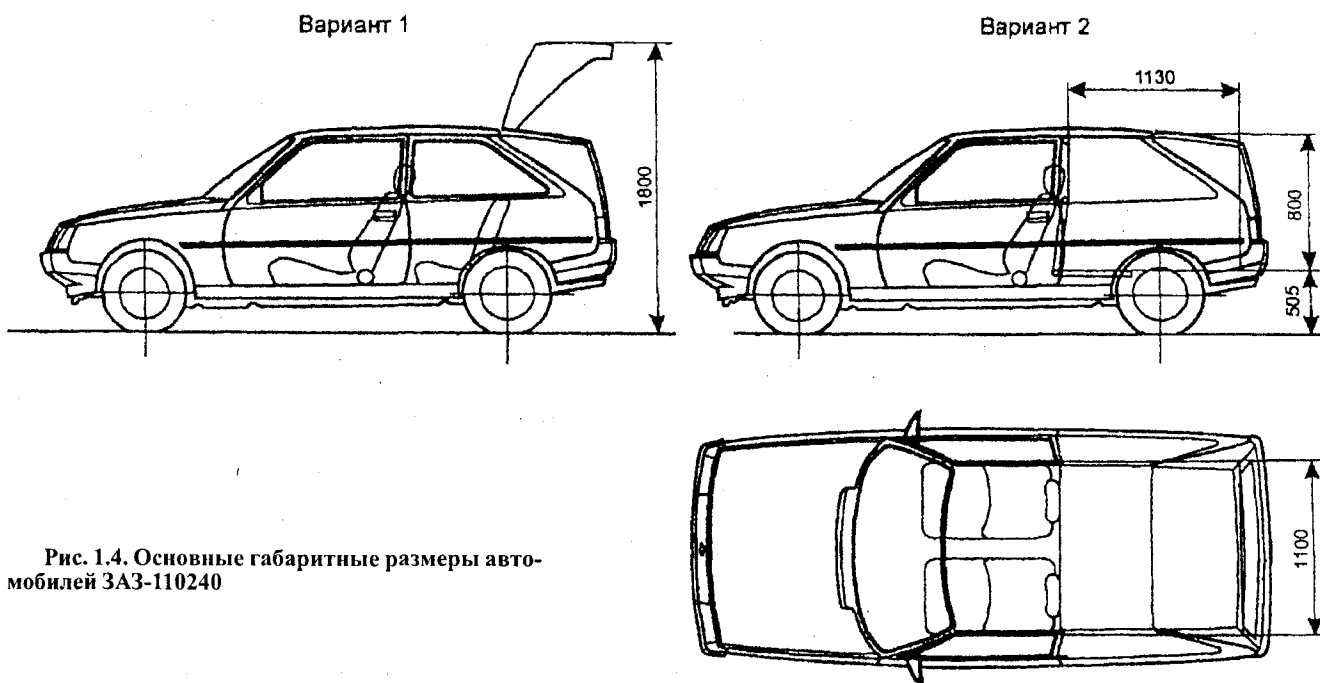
Основные габаритные размеры автомобилей ЗАЗ-110240
